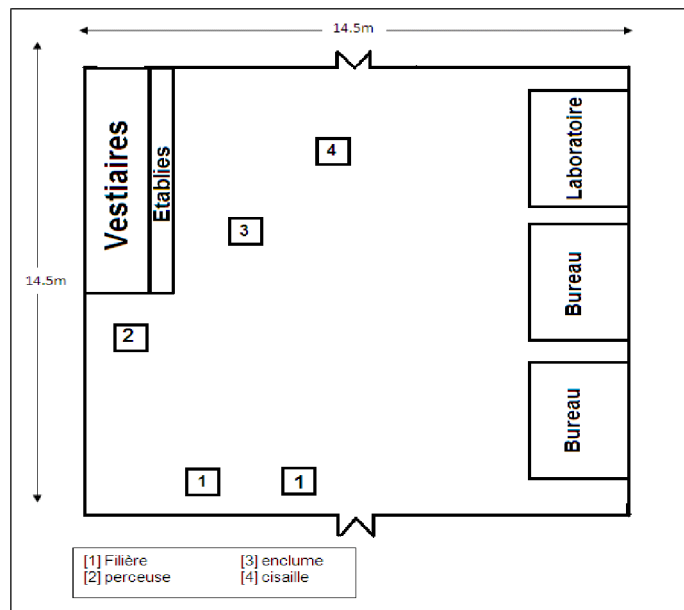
Plan atelier mécano-soudure ENIEM
